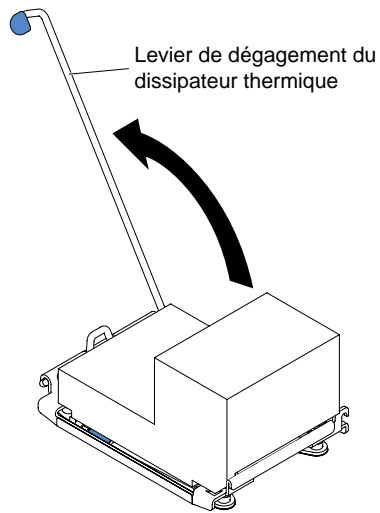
Levier de dégagement du module de fixation du dissipateur thermique
